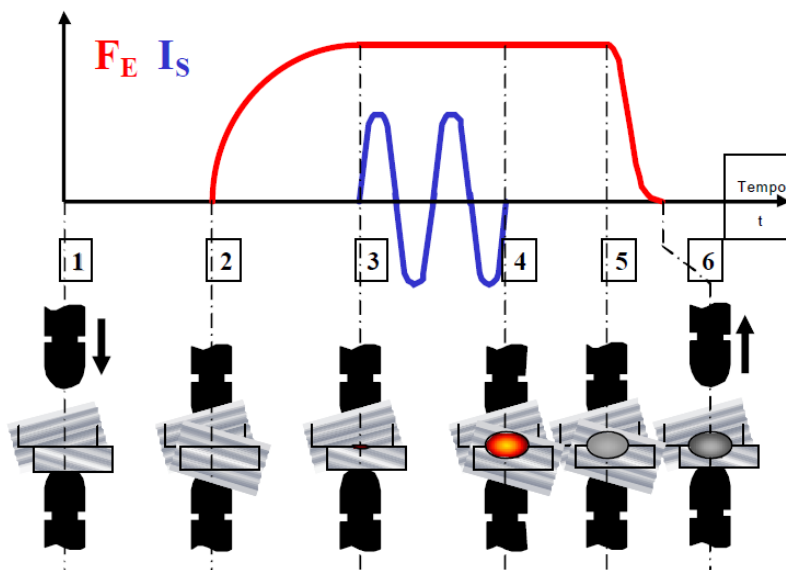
Esquema do ciclo de soldagem de um ponto de solda. (BRANCO, 2004)
